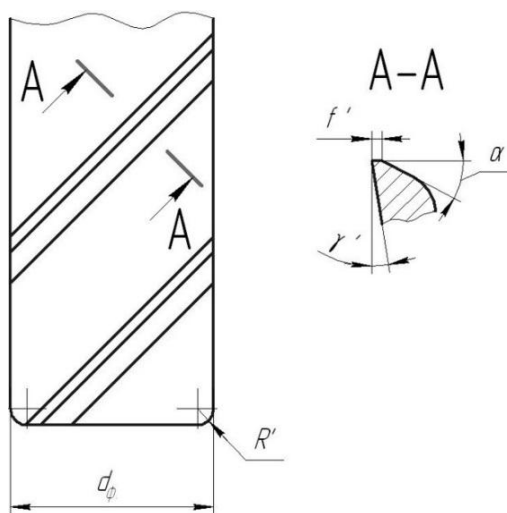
Схема фрезы с геометрической адаптацией режущего клина
